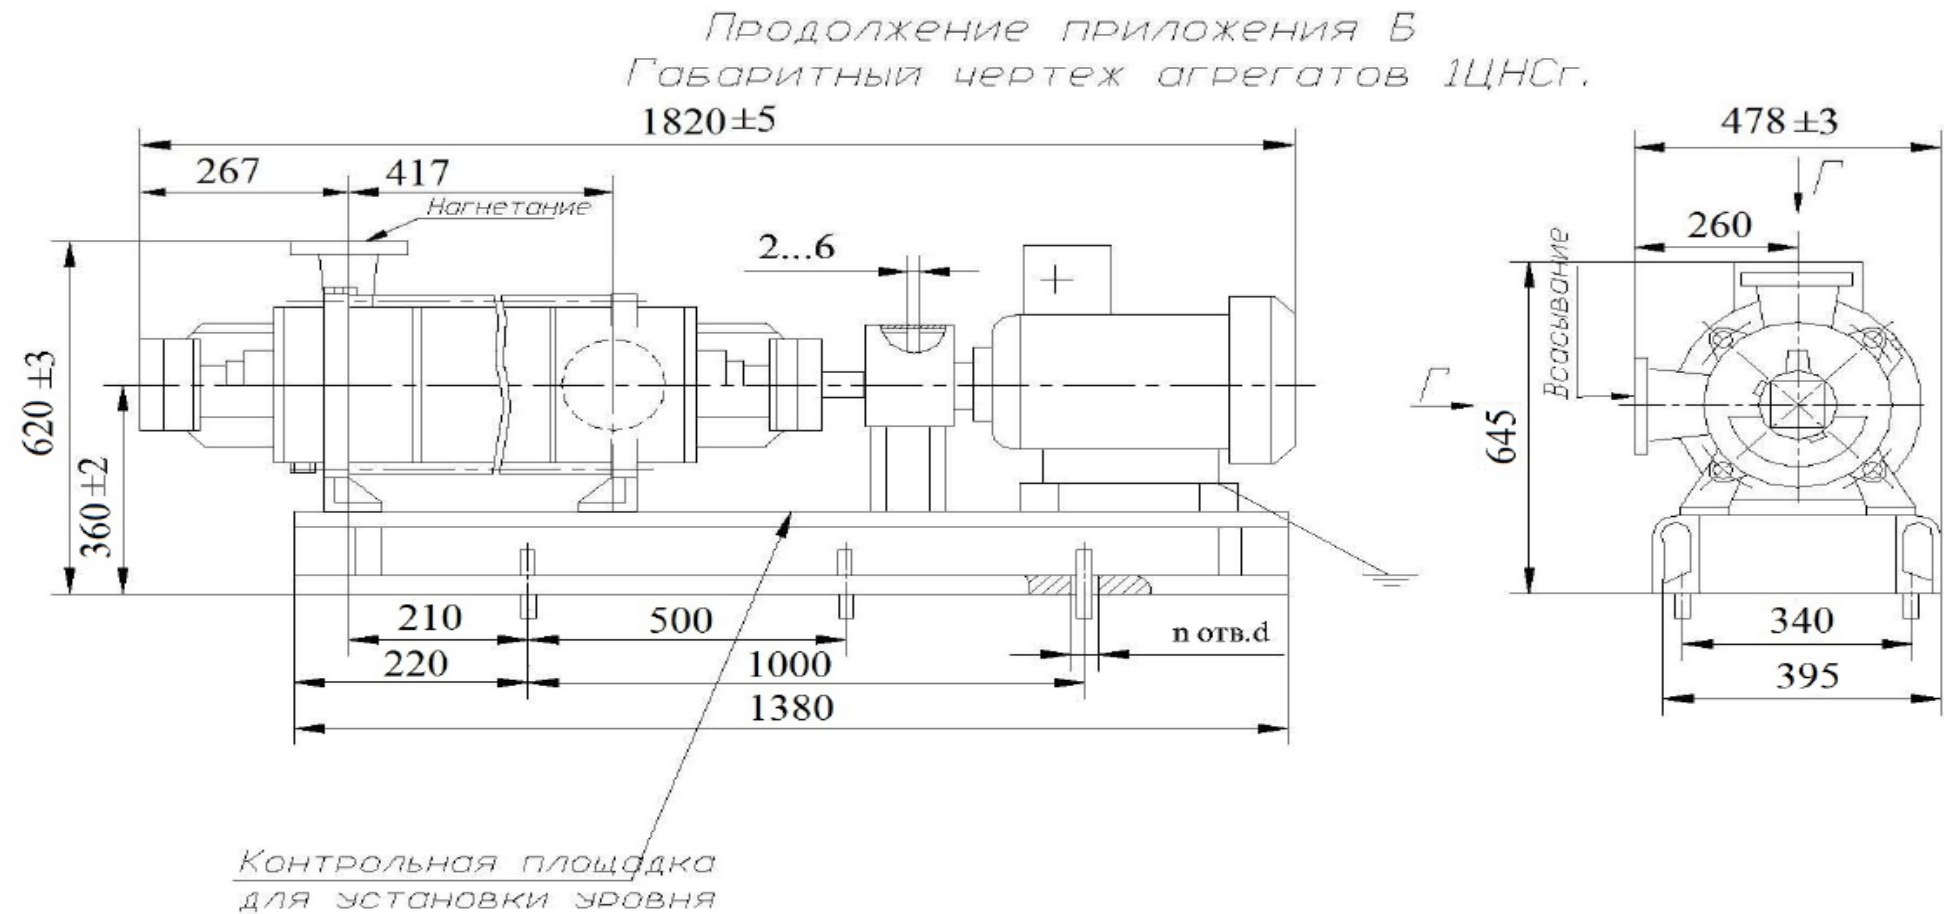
Габаритный чертеж насоса подпитки баков аварийного отвода тепла СПОТ и топливного бассейна JNB50AP001
